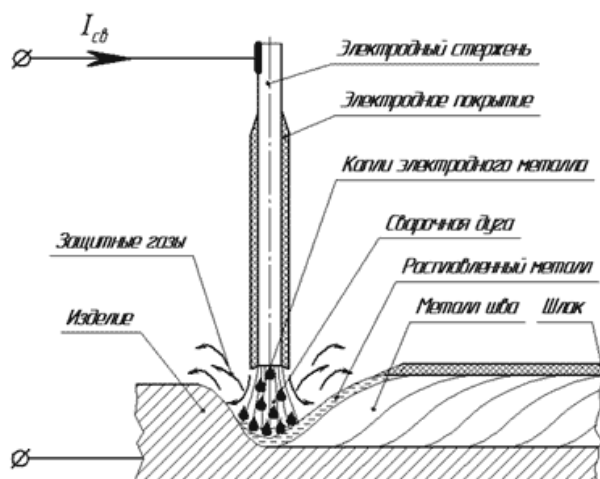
ручная дуговая сварка покрытым электродом, схема и процесс
